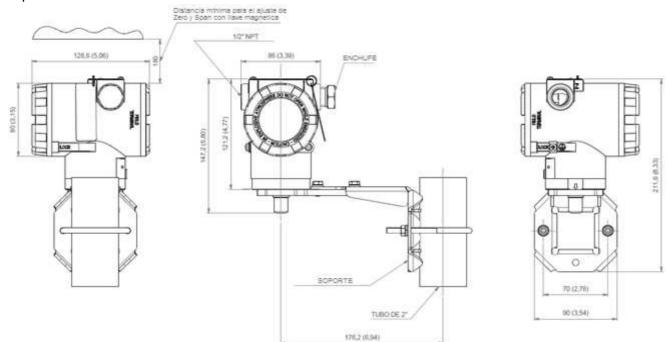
Esquema de dimensiones y montaje de VTP10-H.
